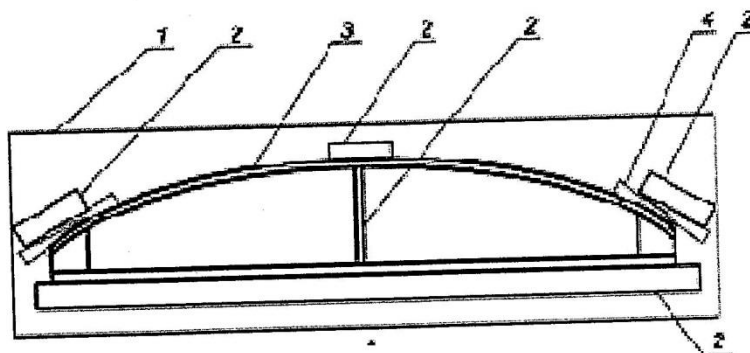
Приспособление для сборки стоек и дуги плечиков на клею
